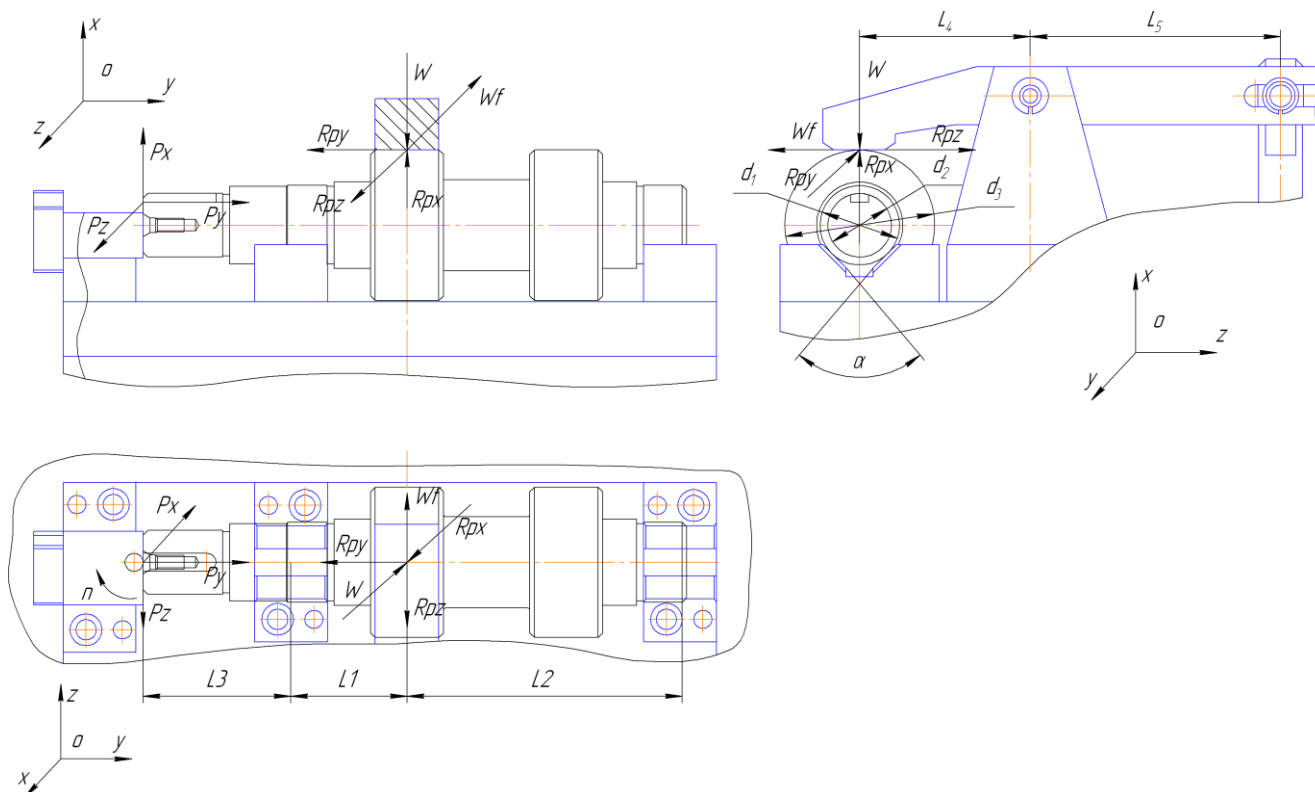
Розрахункова схема дії сил на деталь при фрезеруванні пазів b=8N9
